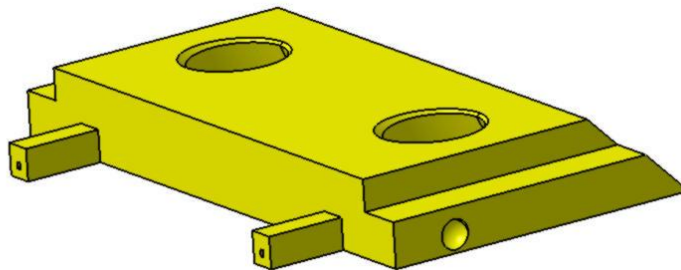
Tvarové jádro pro odformování bočních obdélníkových děr
